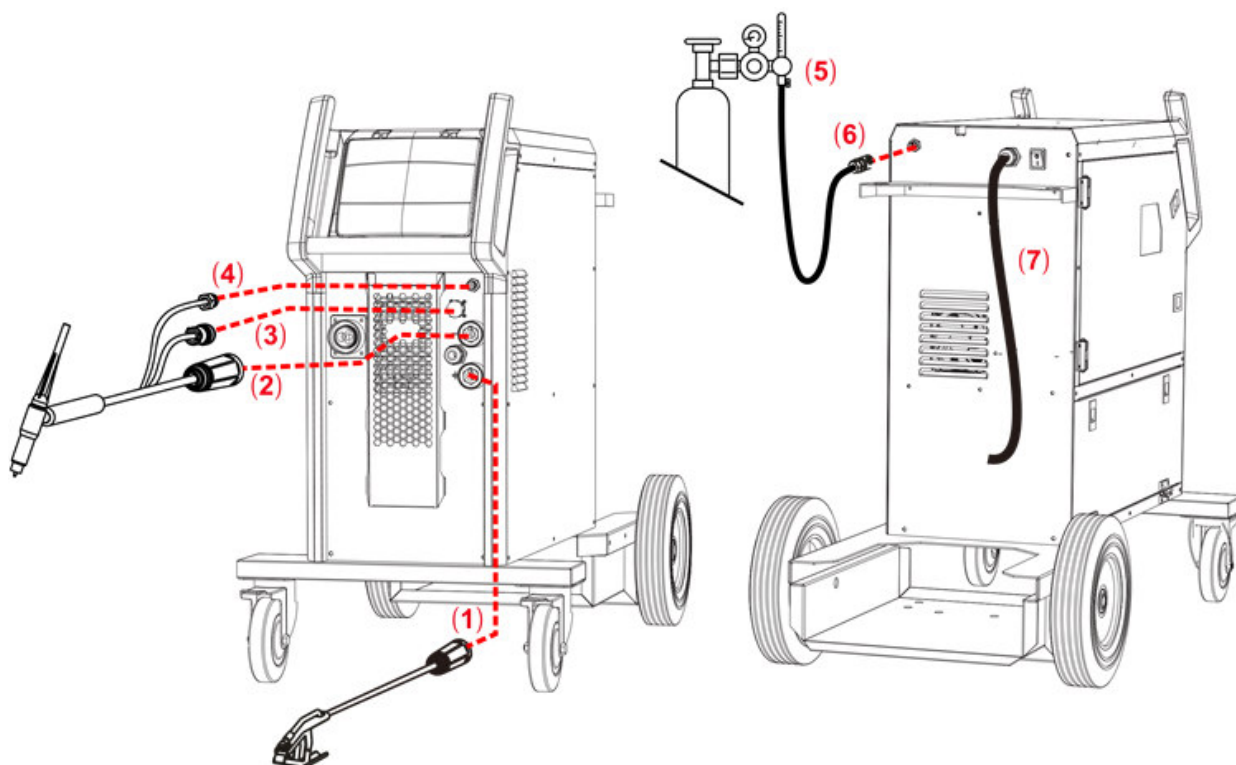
Einrichtung und Installation WIG Schweißgerät
